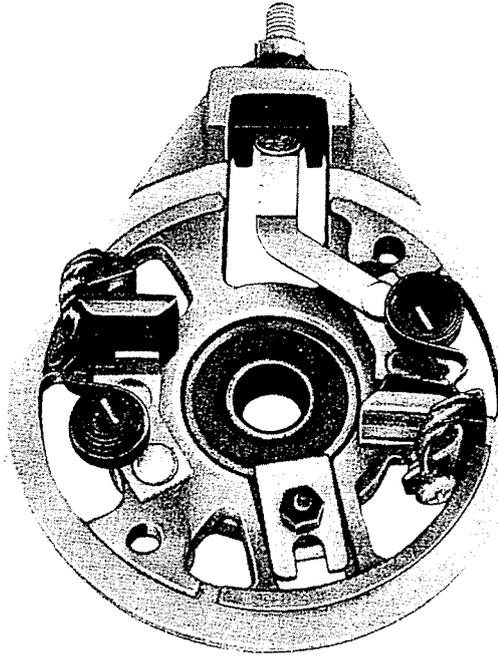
Kollektorlager der Lichtmaschine DSV 90/12/16/3S.
